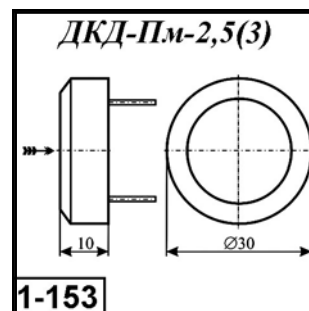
Внешний вид и габаритные размеры детектора ДКД-Пм-2,5-3
